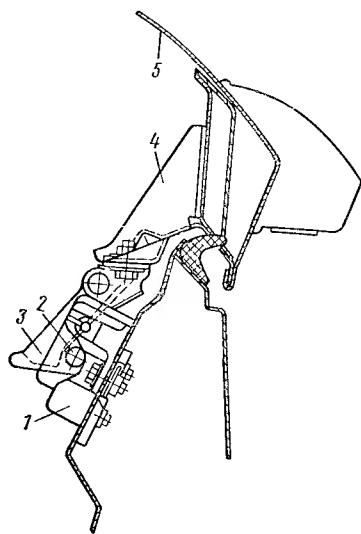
Регулировка крепления замка крышки багажника автомобиля «Москвич-408»
